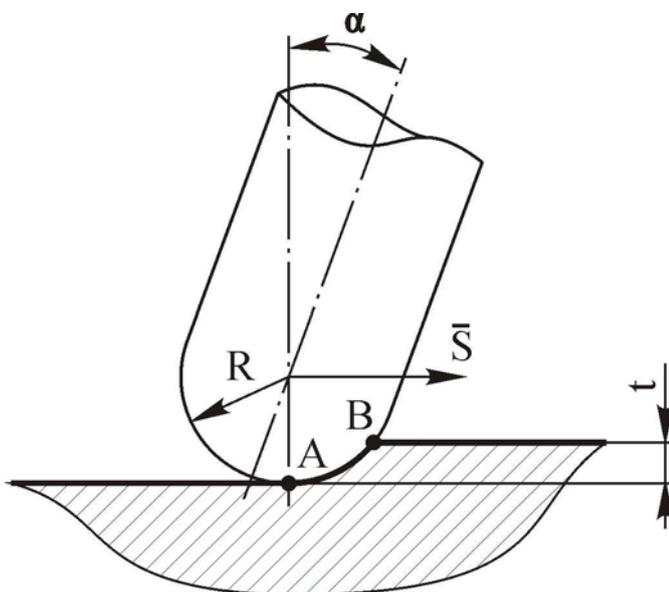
Изменение дуги контакта АВ инструмента и заготовки при наклоне фрезы
